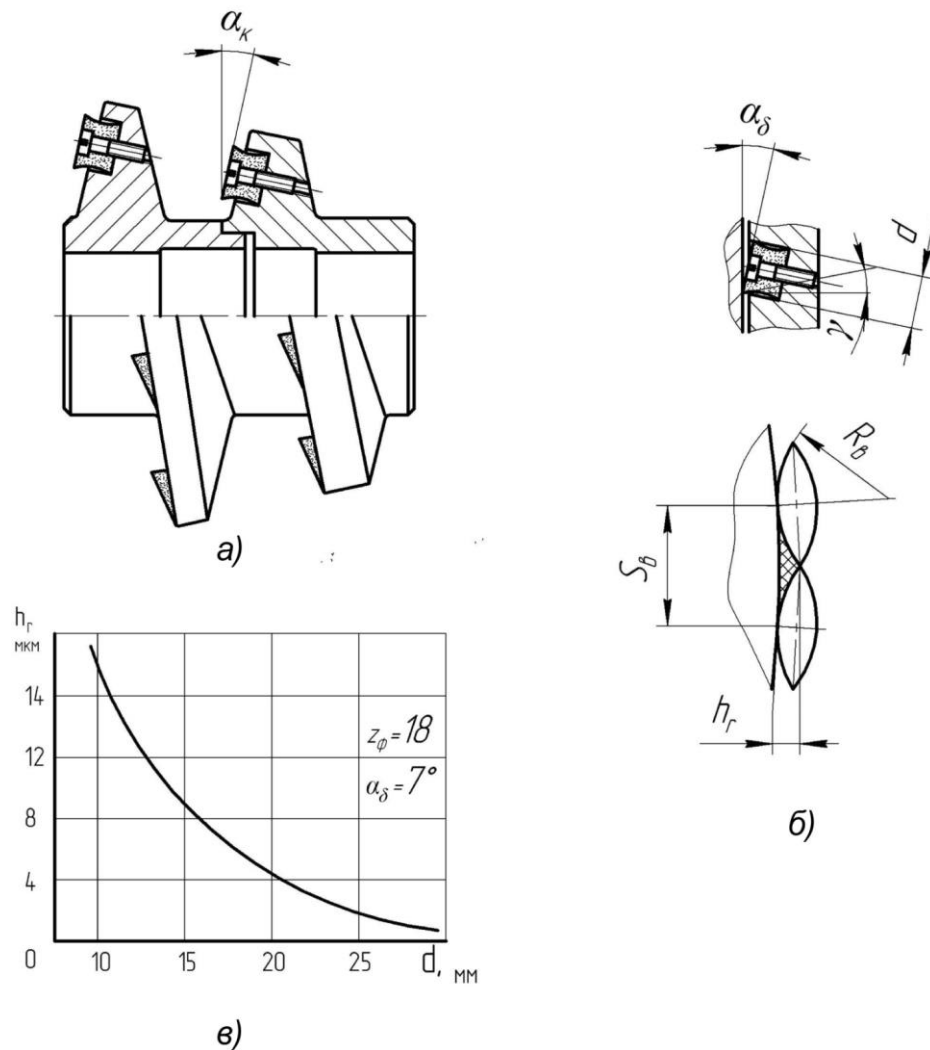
Черв'ячна фреза з роздільною схемою формоутворення з поворотними непереточуваними різальними елементами – вальцями; а - загальний вигляд правого корпусу фрези; б - утворення гребінця нерівності в процесі обкатування зуба колеса; в - залежність висоти нерівностей від діаметру різального елемента – вальця
